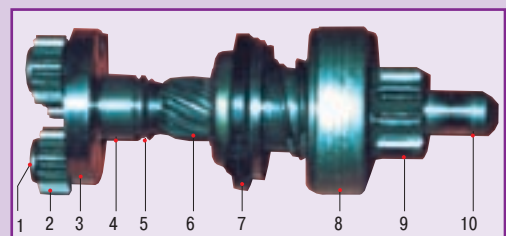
Приводной механизм стартера BOSCH-DW:12/1.1: 1 — ось сателлита; 2 — сателлит планетарного редуктора; 3 — водило на торце вторичного вала; 4 — посадочное место для планетарной шестерни (шестерня снята); 5 — проточка под пружинную защелку; 6 — направляющие спиральные пазы для МСХ; 7 — поводковая муфта; 8 — муфта свободного хода (МСХ); 9 — шестерня МСХ; 10 — вторичный (выходной) вал стартера
